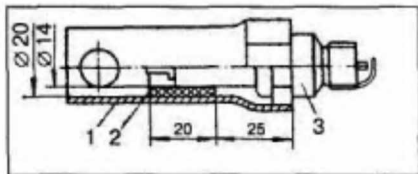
Усовершенствованный свечной ключ: 1 — ключ; 2 — резиновая вставка; 3 — свеча
